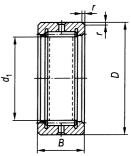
Подшипник роликовый радиальный игольчатый однорядный без внутреннего кольца
